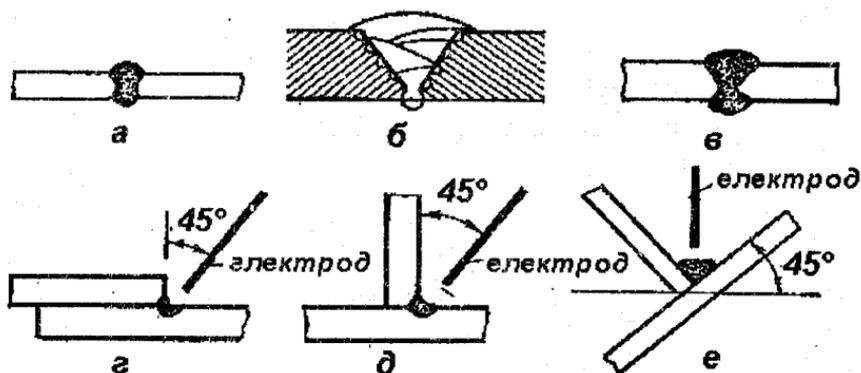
Схеми дугового зварювання залежно від положення заготовок і їх товщини
